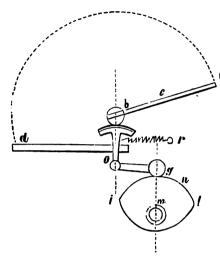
Aelterer Mechanismus gur Bewegung bes mechanischen Auslegers.
